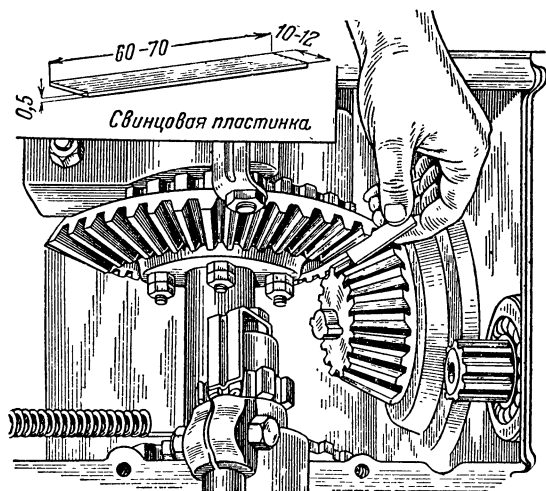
Проверка зазора в зацеплении главной передачи при помощи свинцовой пластинки.
